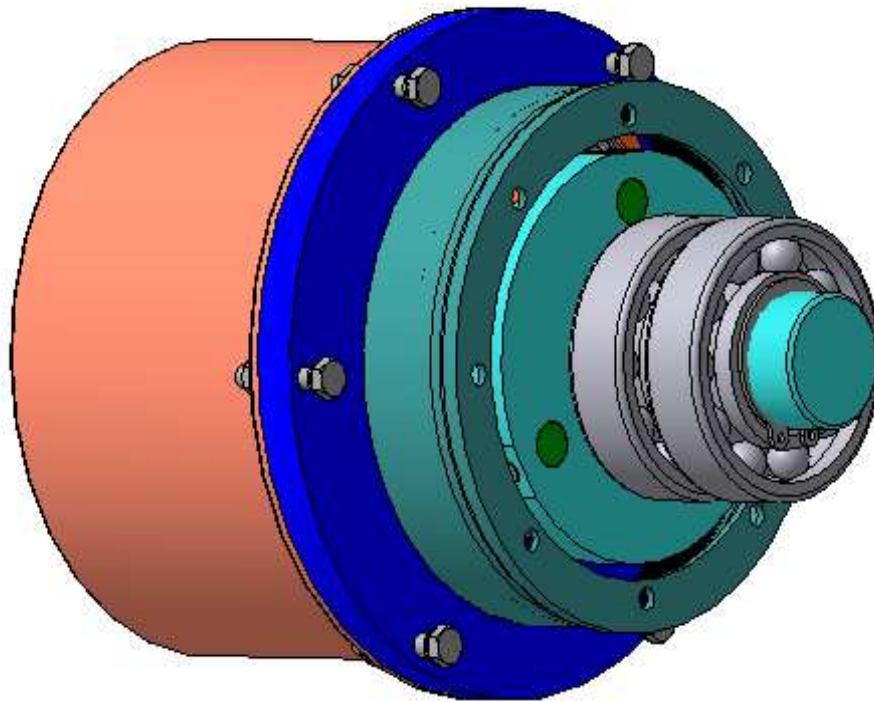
Установка двух шариковых подшипников на выходной вал
